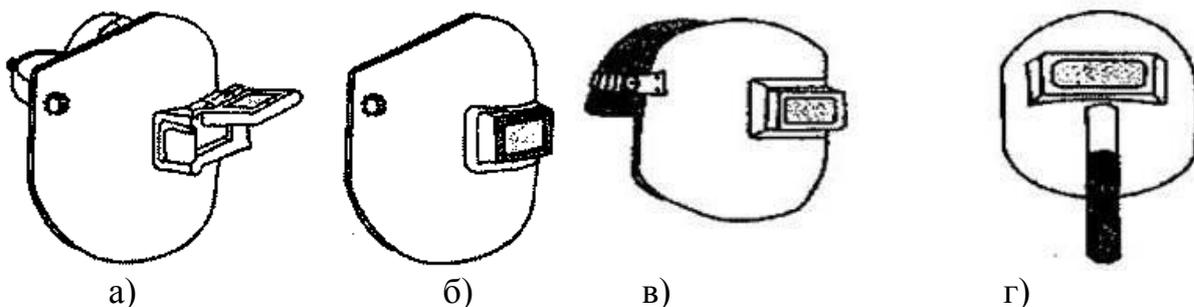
Наголовные щитки для сварочных работ
